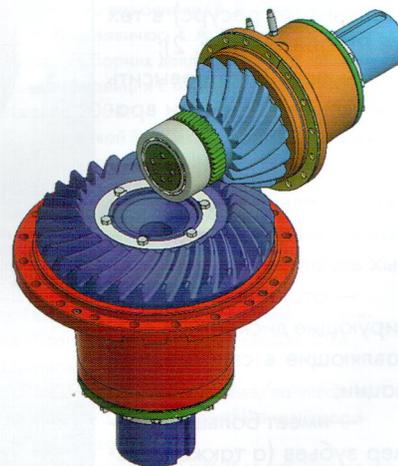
Схема редуктора с ЭЦ-зацеплением
